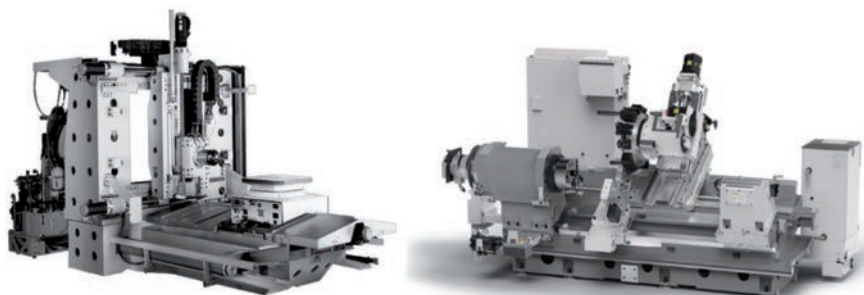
Izda. Un centro de mecanizado horizontal sin carenado.
